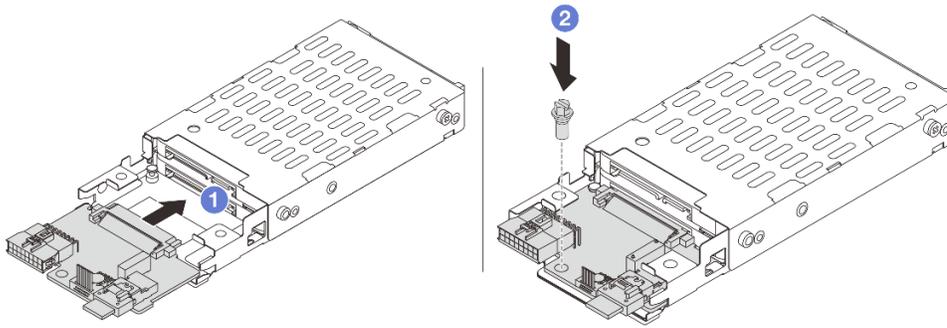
Installation du fond de panier d'unité 7 mm (bas)
